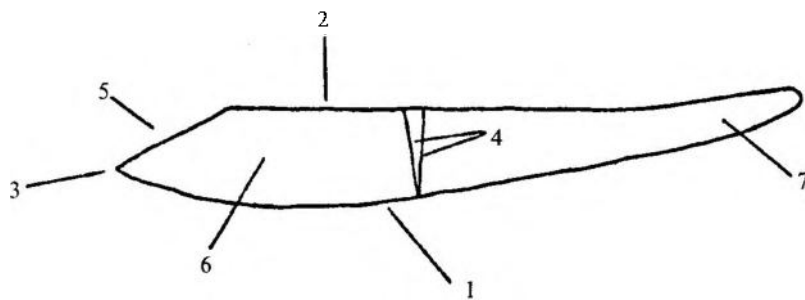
Конструктивные элементы ножа: 1 - лезвие; 2 - спинка; 3 - вершина; 4 - образующие; 5 - конец; 6 - полотно; 7 - держатель
